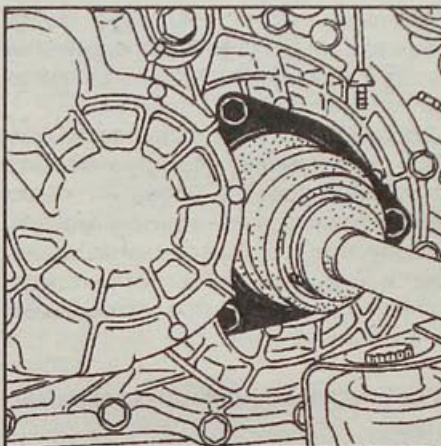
Расположение болтов крепления гофрированного чехла приводного вала на фланце дифференциала
